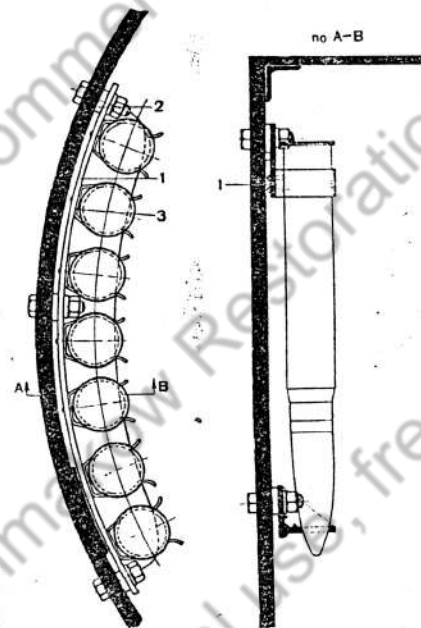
Укладка 45-мм снарядов на стенках башни.
